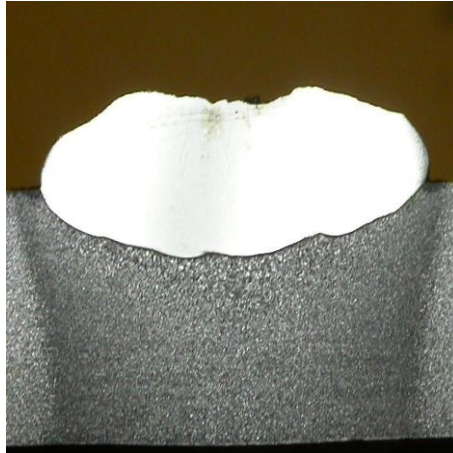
Muestra 3 usando soldadura FCAW con electrodo autoprotegido
